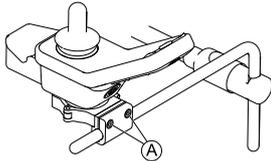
Exemple de réglage DLX-REM400. Les DLX-REM110, DLX-REM211 et DLX-REM216 sont réglés de la même manière.
